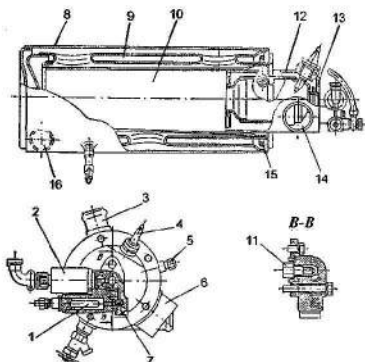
Котел подогрева 1 - электронагреватель топлива; 2 - электромагнитный топливный клапан; 3,16- патрубки отвода жидкости; 4 - свеча зажигания; 5 - патрубок подвода топлива к нагревателю; 6 - патрубок отвода газов; 7 - топливный фильтр; 8 - корпус котла; 9,10- газовые полости; 11 - форсунка; 12 - горелка; 13 - завихритель воздуха; 14 - патрубок подвода воздуха; 15 - нагреватель топлива.
